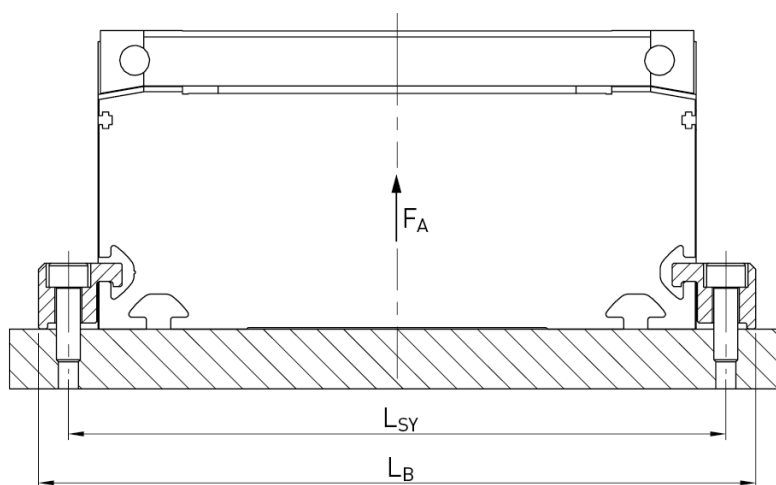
Befestigung mit Spannprofilen – HT100, HT150
